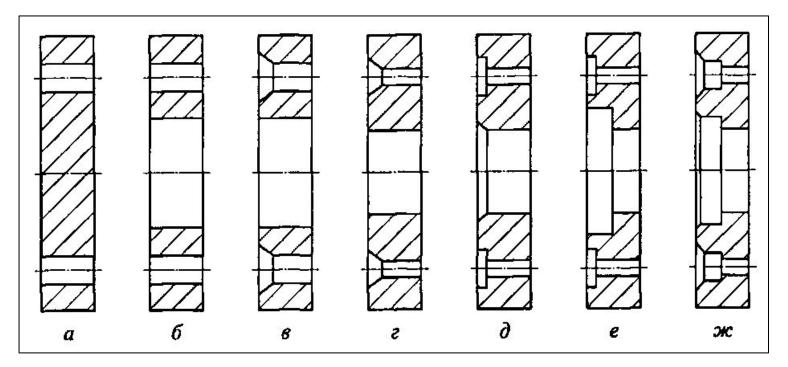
Примеры конструкций: a-e — детали типа фланцевого диска; ж — деталь-представитель
